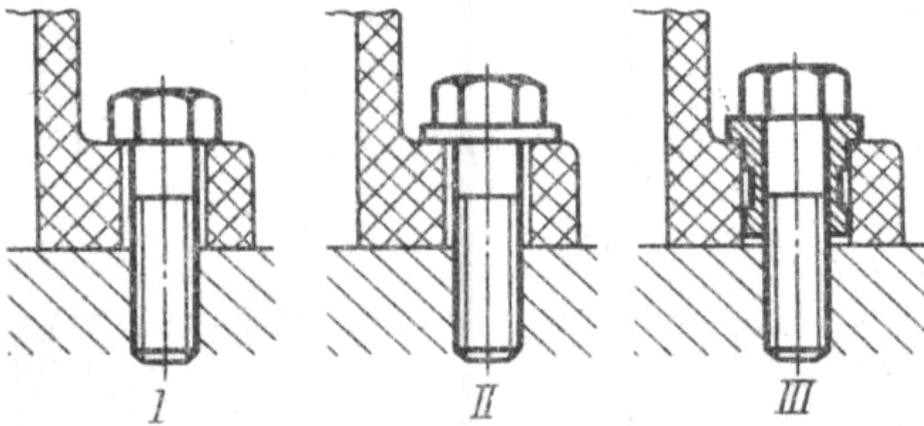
Предупреждение смятия опорных поверхностей под головки крепежных деталей
